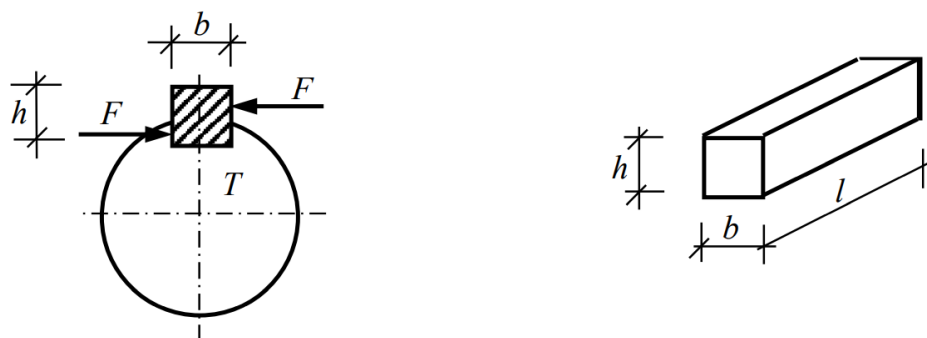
Carregamento e dimensões de uma chaveta. [33]
